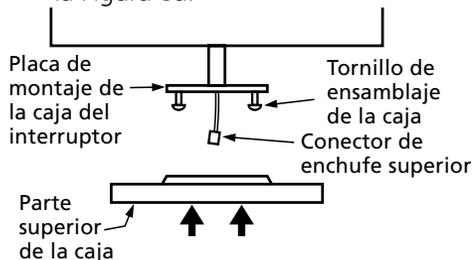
Forma de instalar la parte superior de la caja del interruptor en la placa de montaje de la caja.
